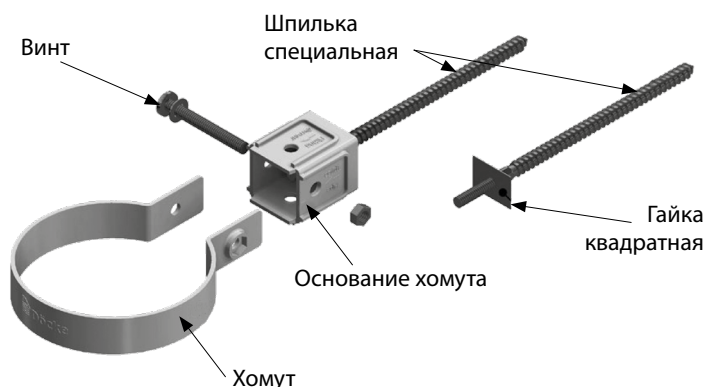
Хомут трубы КОМФОРТ и шпилька с гайкой
